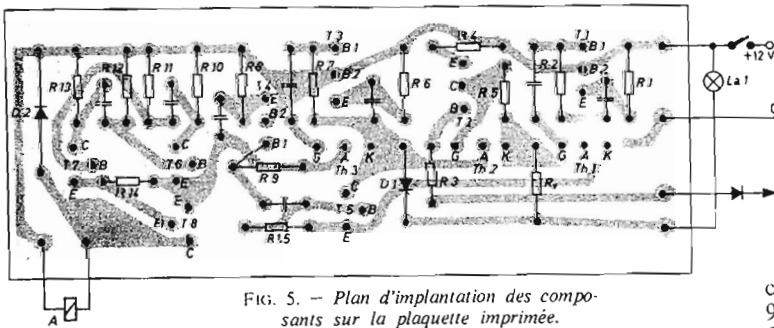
Plan d'implantation des composants sur la plaquette imprimée.
